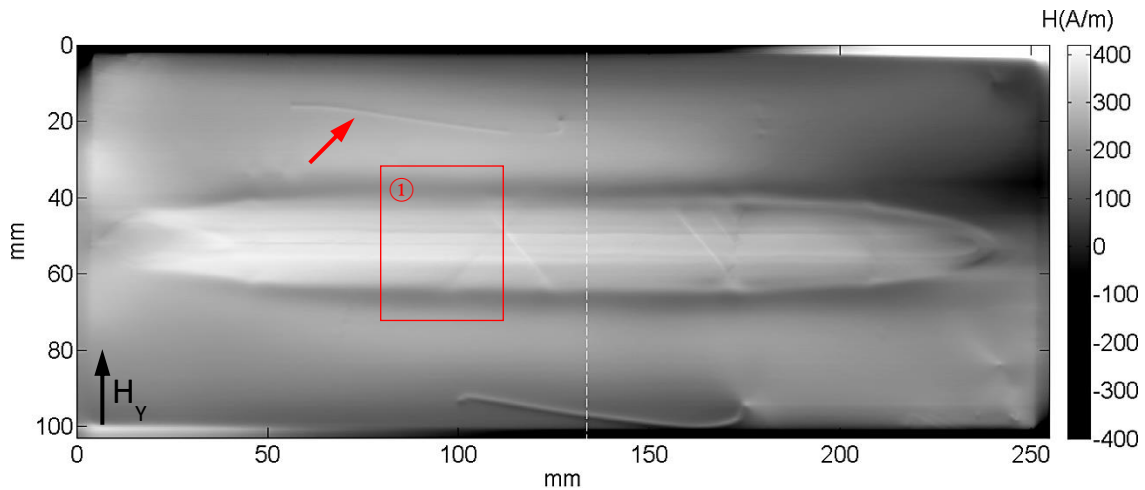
Multilinen GMR Magnetometermessung (\vec{H}_y) einer Blindschweißnaht
